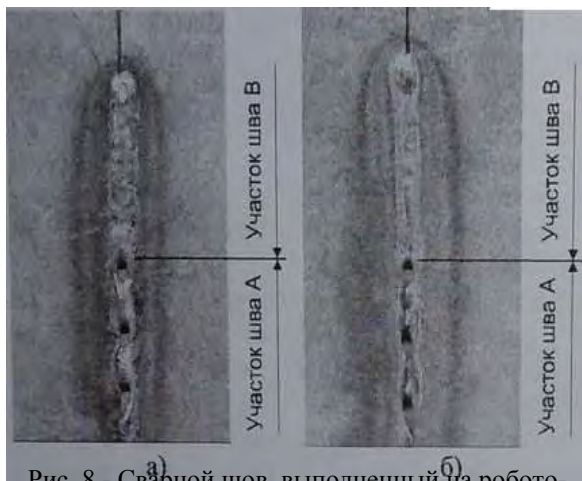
Сварной шов, выполненный на робототехническом комплексе РМ-01: а) лицевая сторона шва; б) обратная сторона шва
